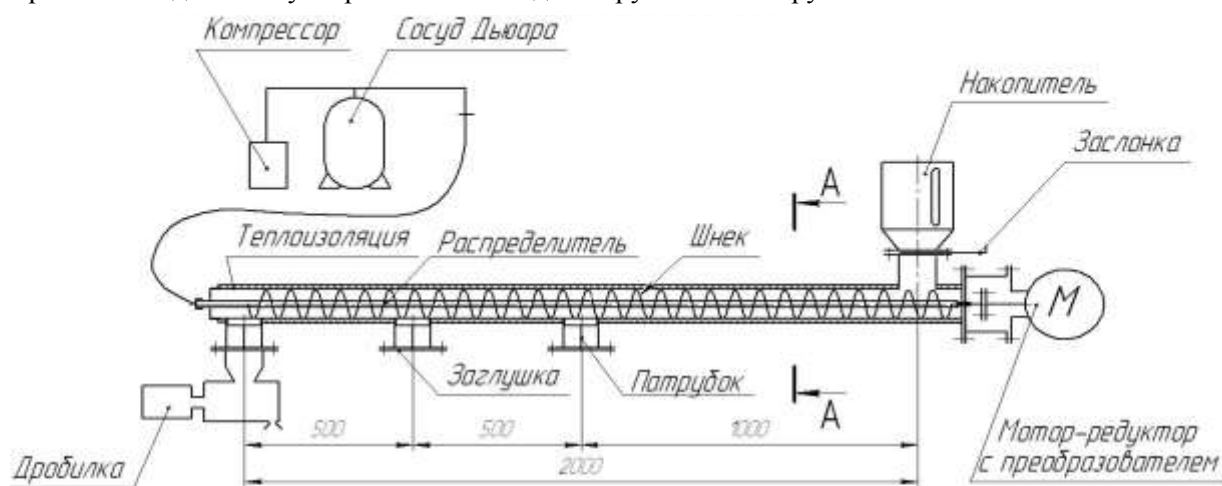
Схема лабораторной установки для исследования процесса транспортирования и измельчения пряноароматического сырья
